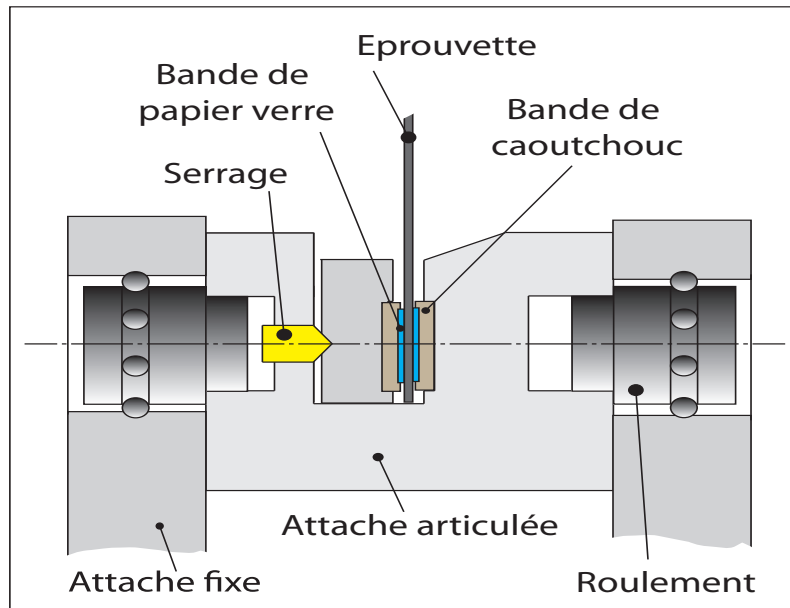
Schéma de montage de l'éprouvette sur la machine d'essai.
